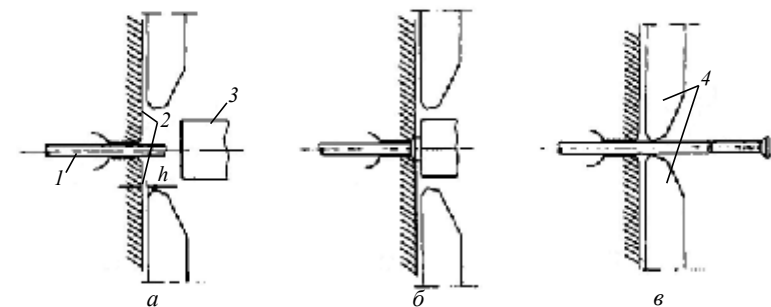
Схема процесса изготовления проволоочных гвоздей на пресс-автомате:
